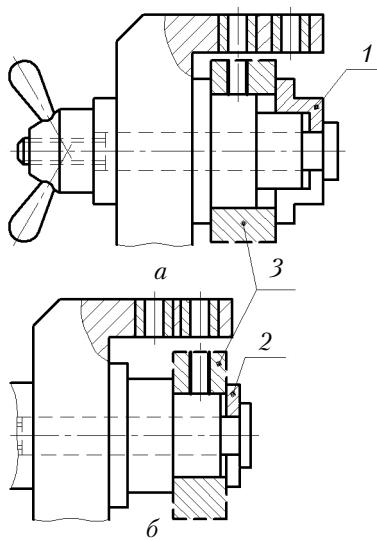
Кондуктор для сверления отверстий в кольцах
